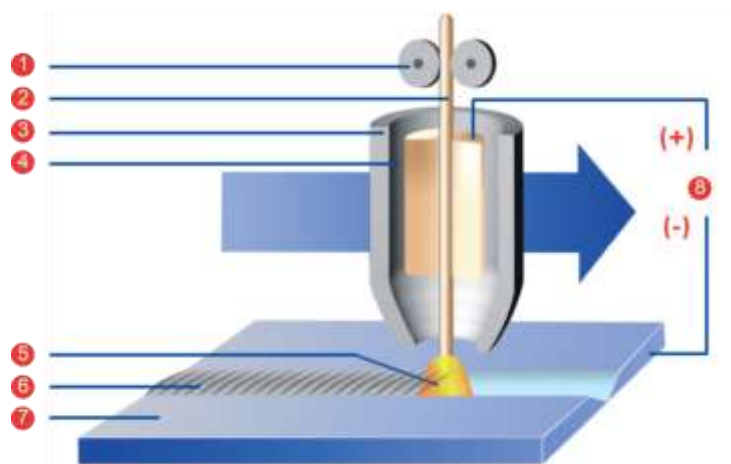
Схема напіваавтоматичного зварювання в захисному газі
